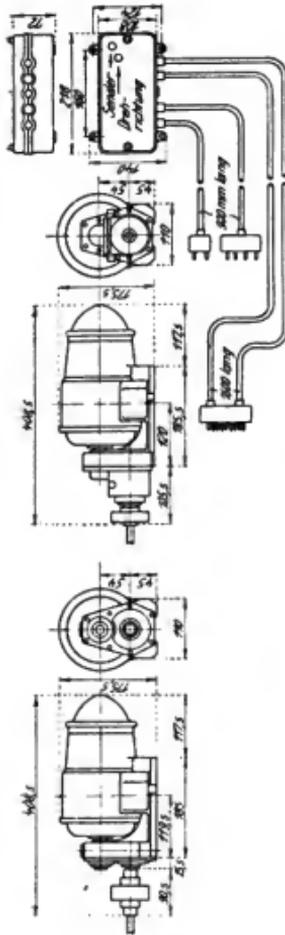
Wechselstrommaschine D/17 mit Vorgelege Type A 17 und B 18 sowie zugehörigen Schaltkasten.
